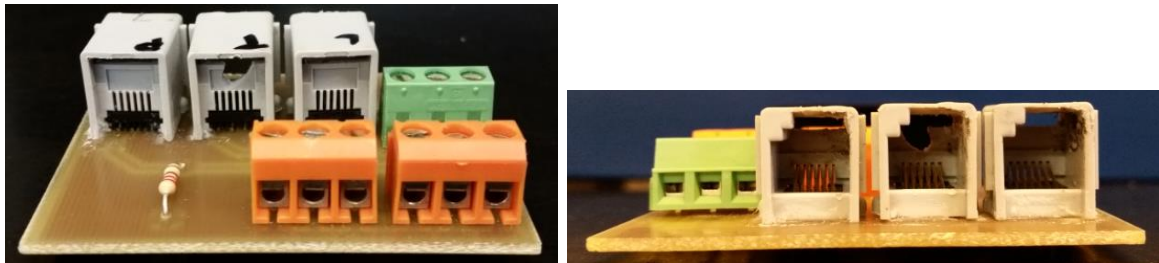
Vistas frontal y lateral de PCB conexión NXT
